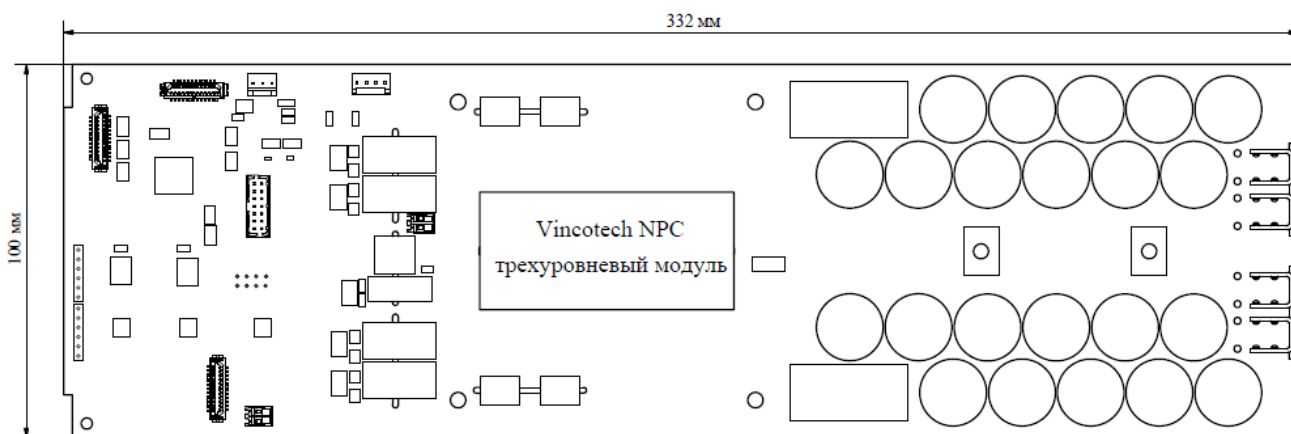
Габаритный чертеж печатной платы одной стойки NPC
